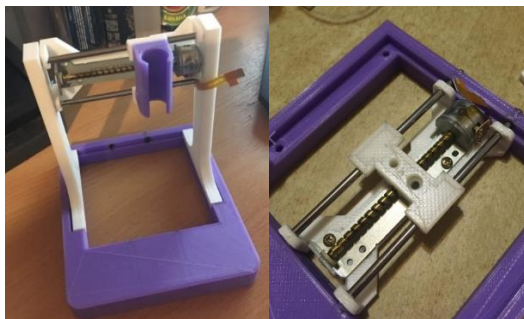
Сборка корпуса и ходовой части оси x и оси y
